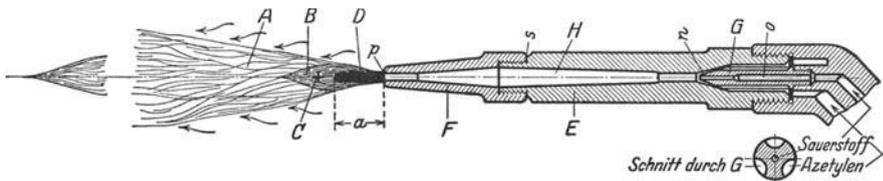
Vorderteil des Azetylenbrenners mit Schweißflamme.
